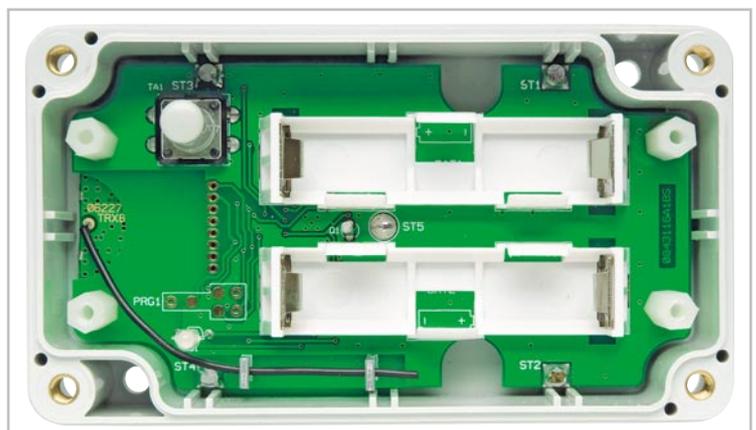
Die komplett bestückte und im Gehäuseunterteil verschraubte Platine
